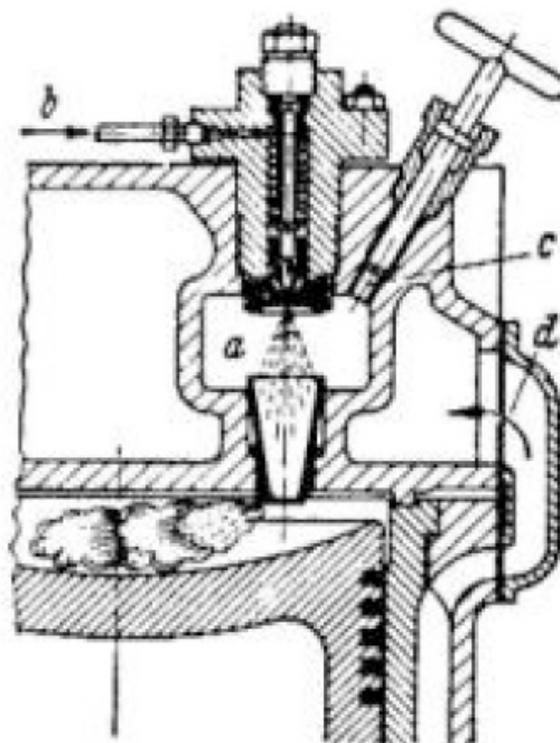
Esquema básico da injeção indirecta. "a" antecâmara, "b" entrada de combustível, "c" ignição auxiliar para partidas a frio, "d" passagem de água de refrigeração para o cabeçote.
